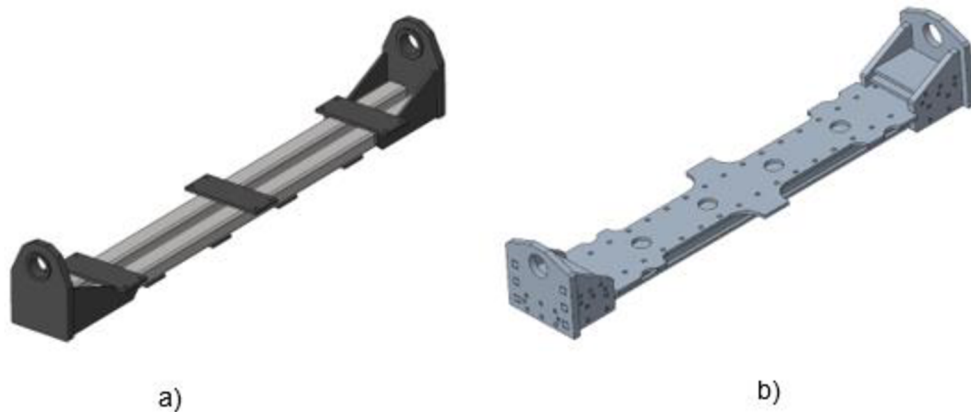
Stávající technické zařízení (podklady KSR)
